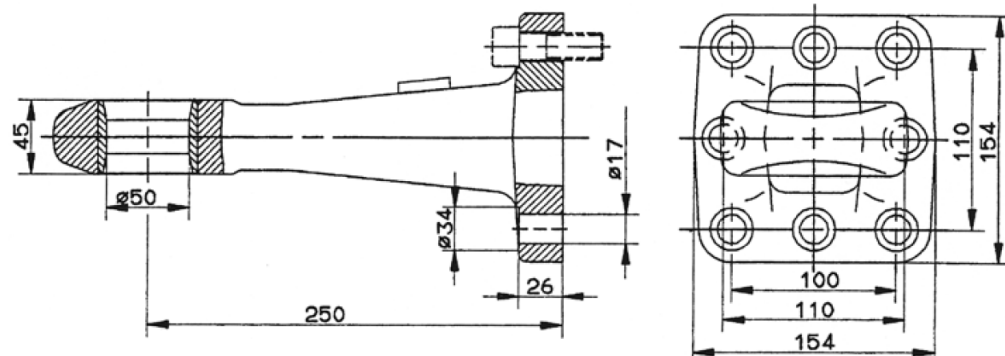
Ringfeder tažné zařízení typ 5055A [25, s.22]
